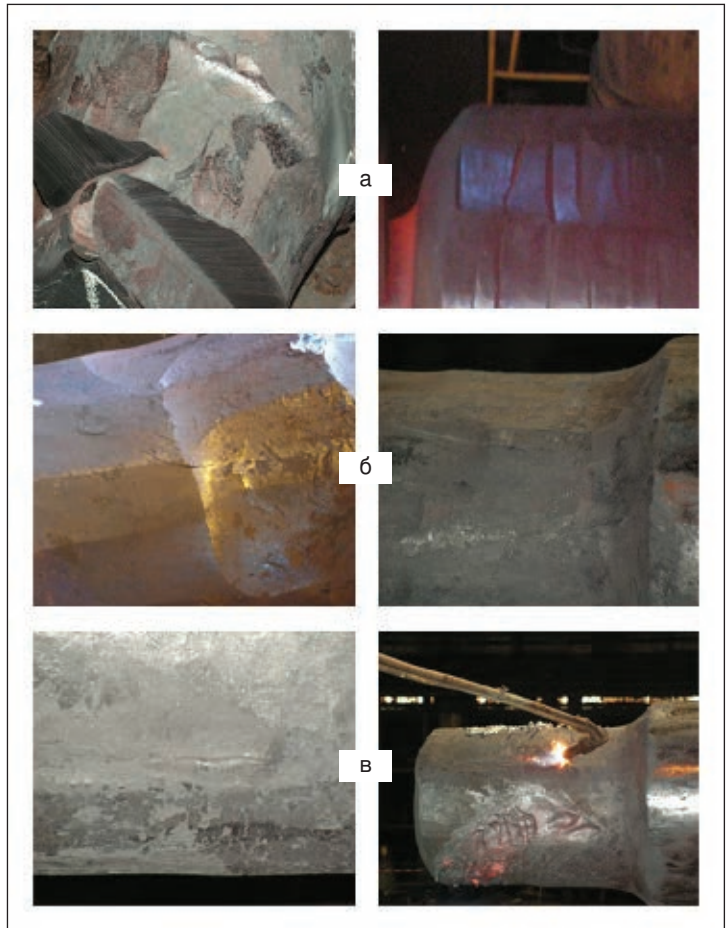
Основные виды дефектов на поковках, подлежащих выплавке в процессе изготовления заготовки: а — зажимы; б — трещины; в — плены
